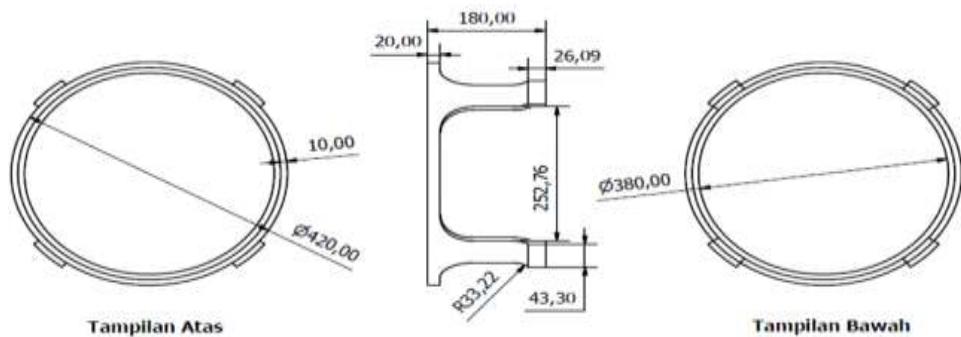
Tutup Tabung Reaktor 2 (3dimensi)
